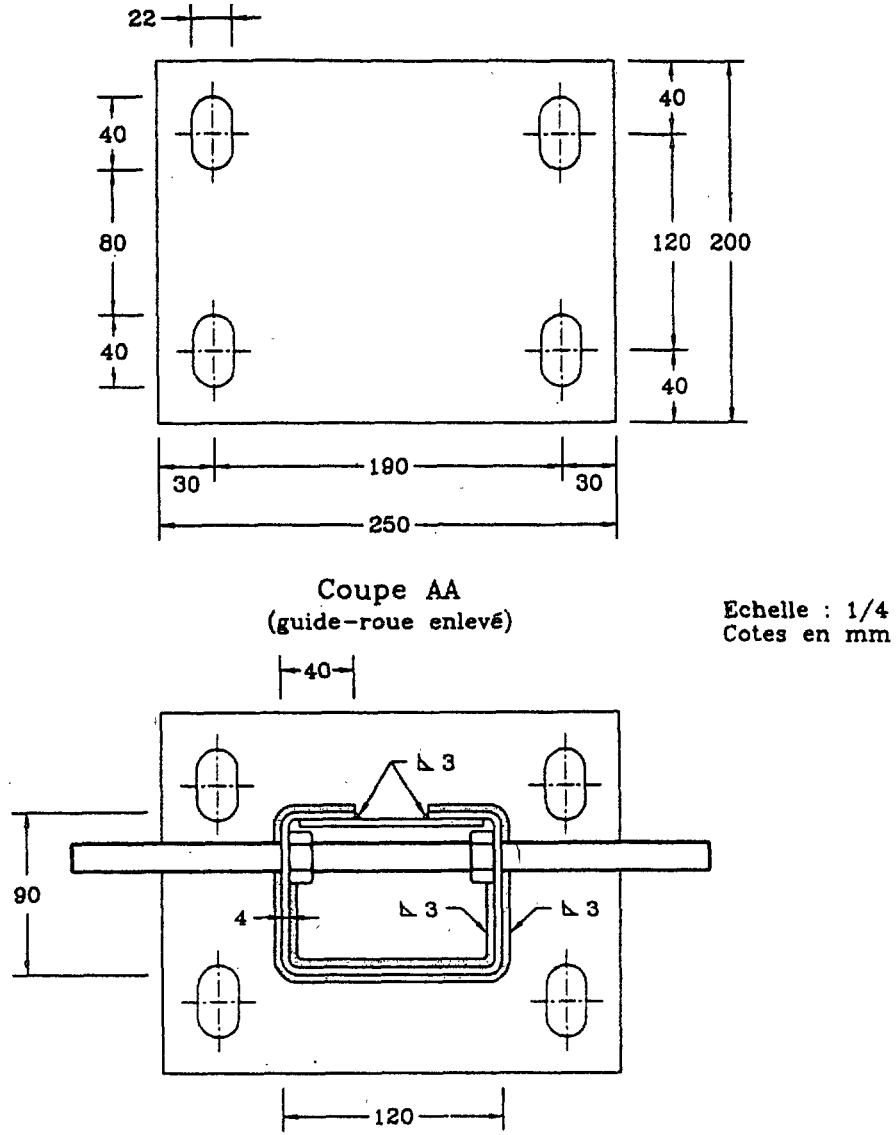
DETAIL DES PIÈCES D'ANCRAGE
